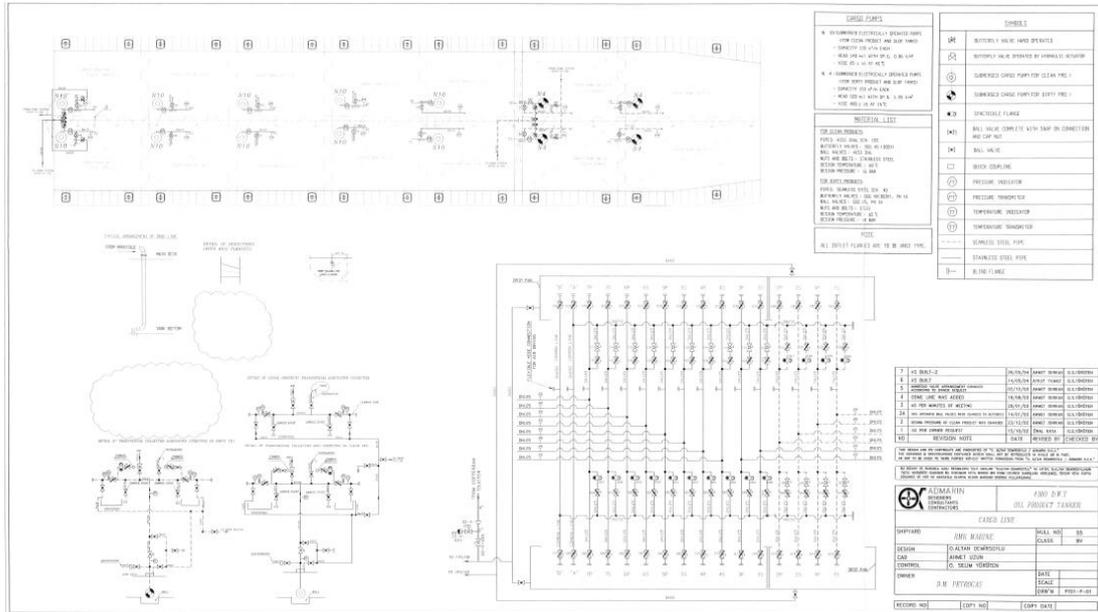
Plano líneas de carga. Fuente: Trabajo de campo.
